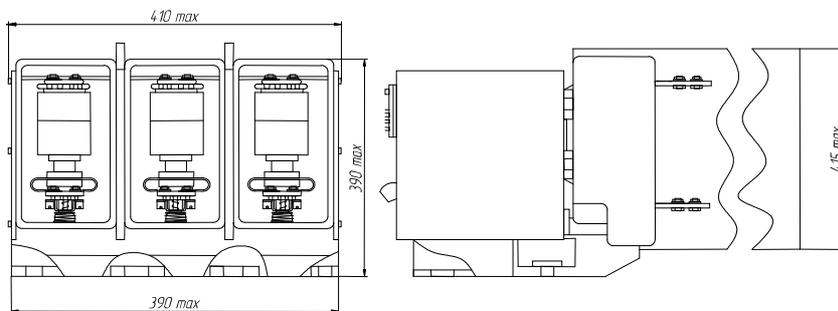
Габаритные и установочно-присоединительные размеры выключателя (стационарное исполнение)
